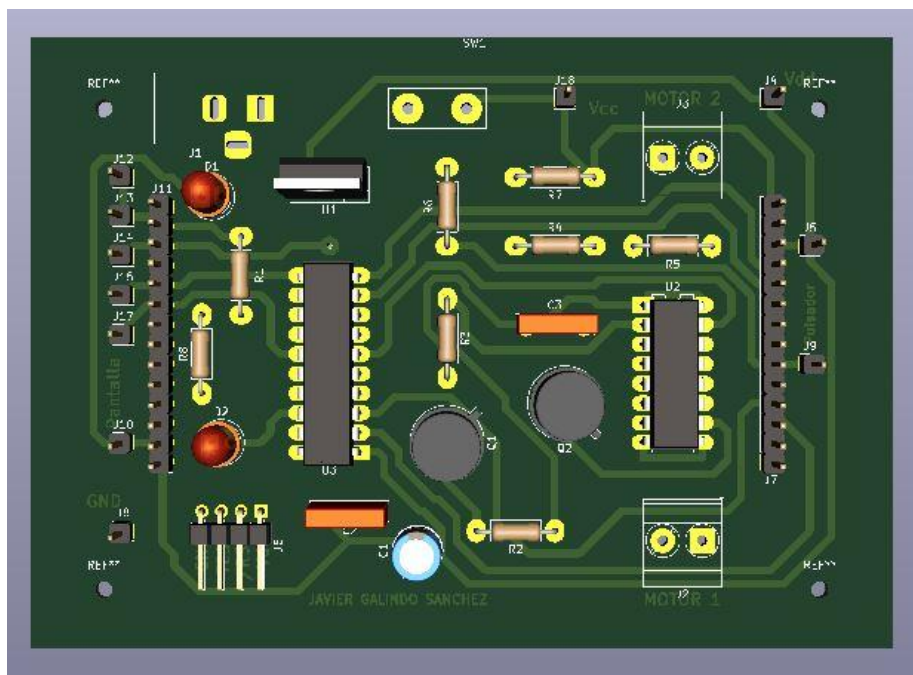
Vista 3D del diseño completo del módulo motor.
